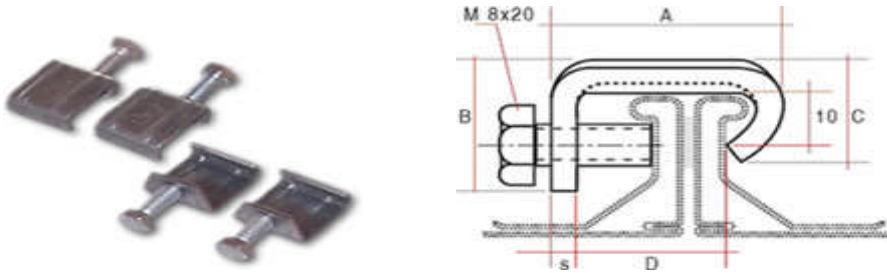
Montajda kullanılan köşe tespit elemanı
